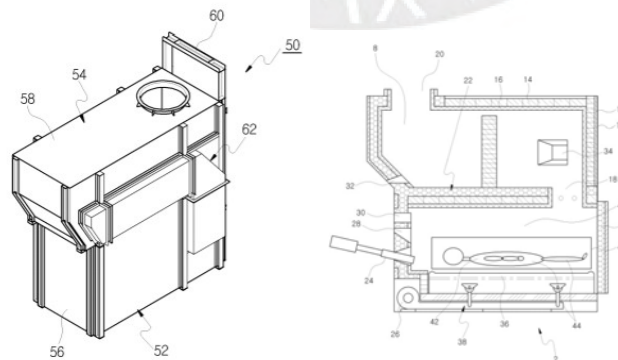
Vista isométrica del crematorio(izquierda) y vista de corte (derecha). Fuente:
